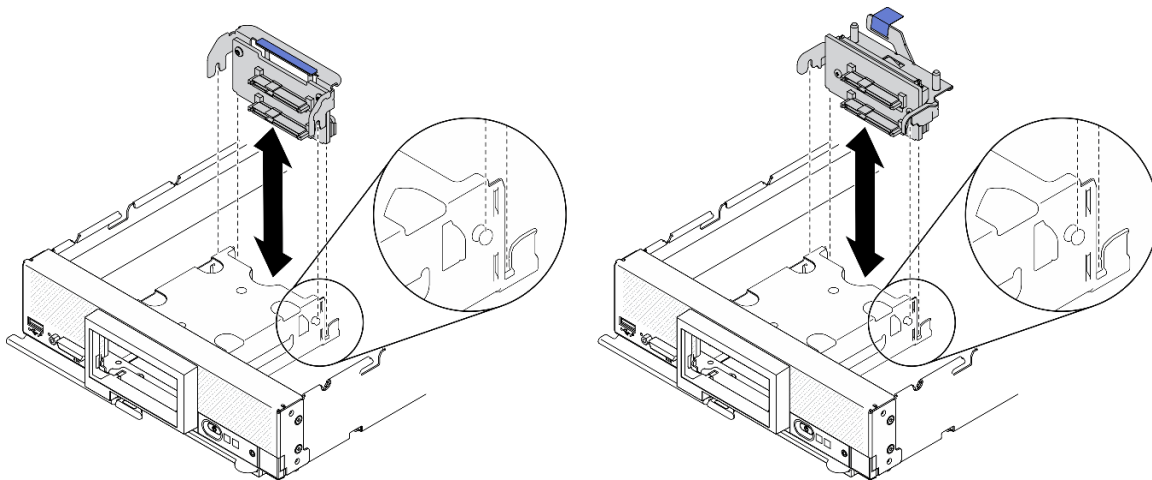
Installation d'un fond de panier d'unité 2,5 pouces
